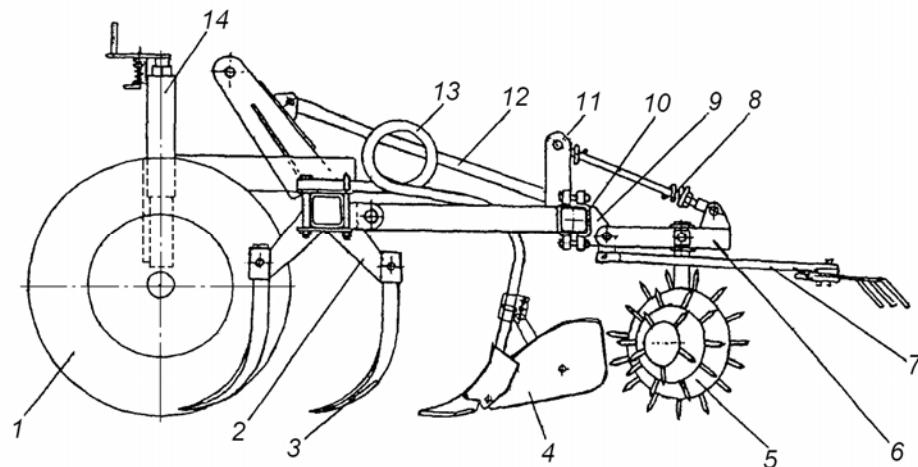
Культиватор-окучник-гребнеобразователь ОКГ-4 (вид сбоку):
